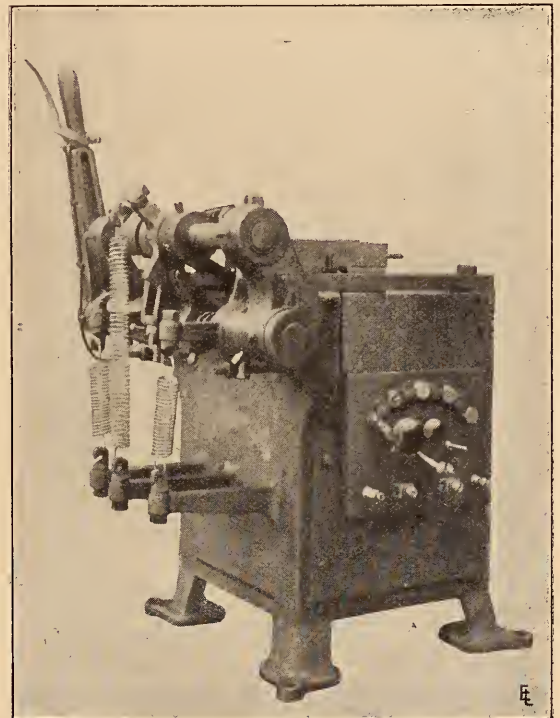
Machine à souder les maillons et boucles (Languepin).
